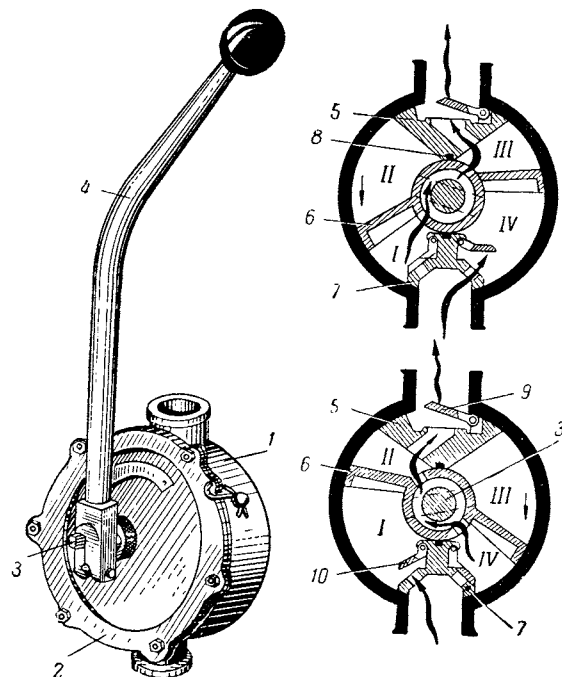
Ручной топливоподкачивающий насос РНА-1:
